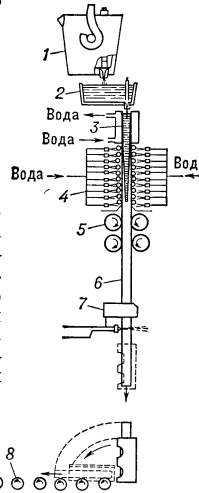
Принципиальная схема УНРС: 1 — сталеразливочный ковш; 2 — промежуточный ковш (предназначен для снижения и стабилизации напора металла, поступающего в кристаллизатор, и для распределения металла по нескольким кристаллизаторам на многоручьевых установках); 3 — кристаллизатор; 4 — зона вторичного охлаждения с устройствами для направления заготовки и подачи воды; 5 — тянущие валки; 6 — слиток; 7 — устройство для резки заготовки (кислородные резаки или ножницы); 8 — устройство для выдачи заготовки.
